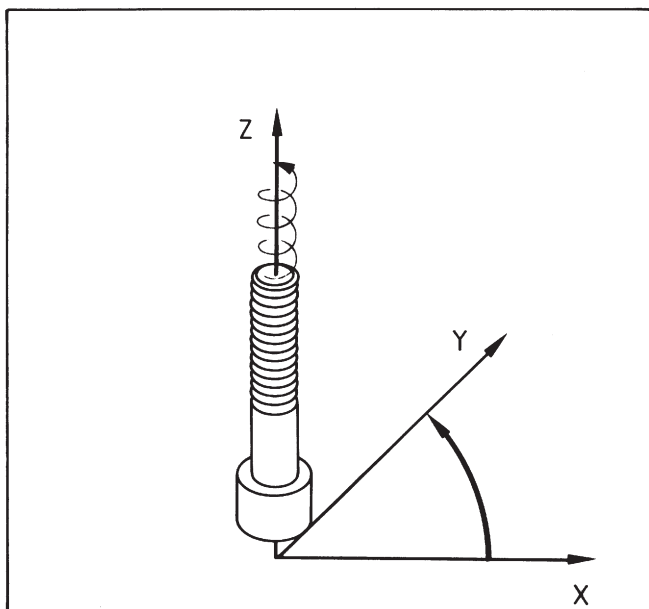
Positive Drehbewegung (Schraube mit Rechtsgewinde)
